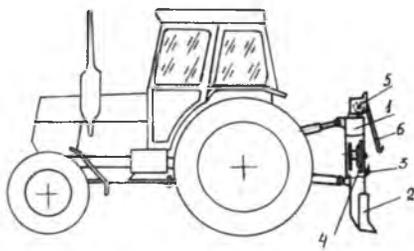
Схема приспособления трелевочного навесного ПТН-10А с трактором ЛТЗ-55:
